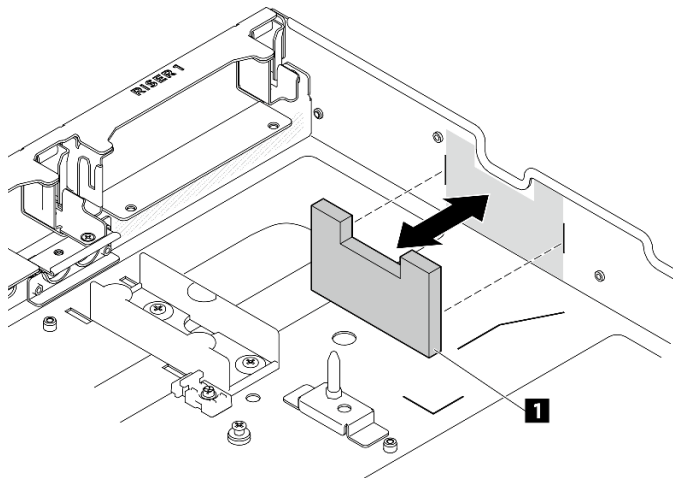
Entfernen der DPU-Luftführung aus dem Gehäuse
